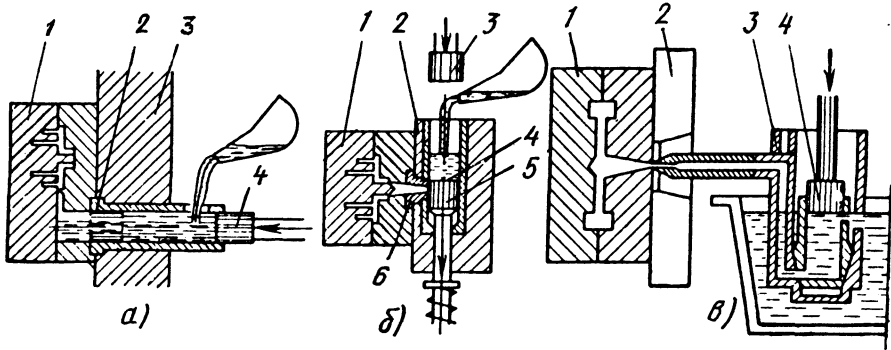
Основные типы камер прессования машин ЛПД:
